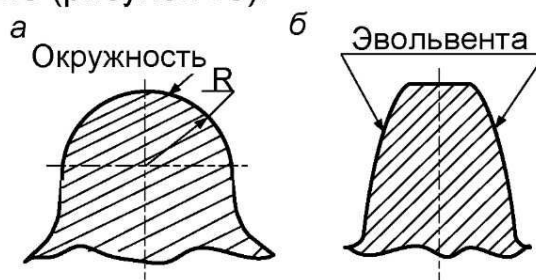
Профиль зубьев: а - круговой; б - эвольвентный
